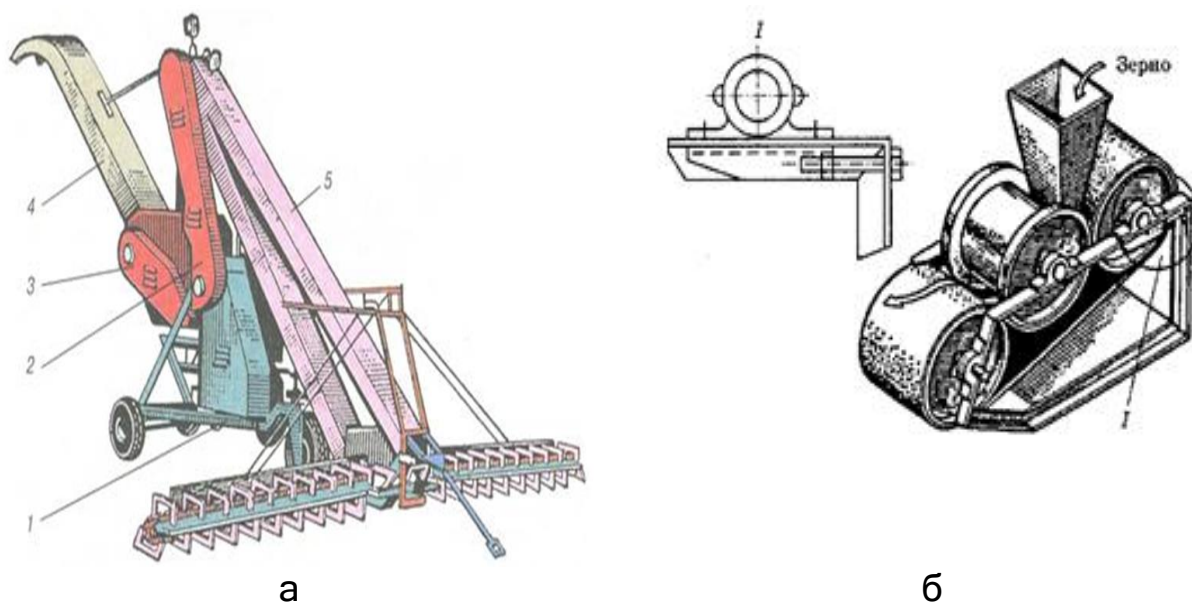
Зернометальник самопересувний ЗМ-60: а - загальний вигляд: 1 - рама з ходовою частиною; 2- контрпривід; 3- тример; 4 - напрямний кожух з козирком; 5 - завантажувальний конвеєр; б - загальний вигляд тримера: І - натяг стрічки.
